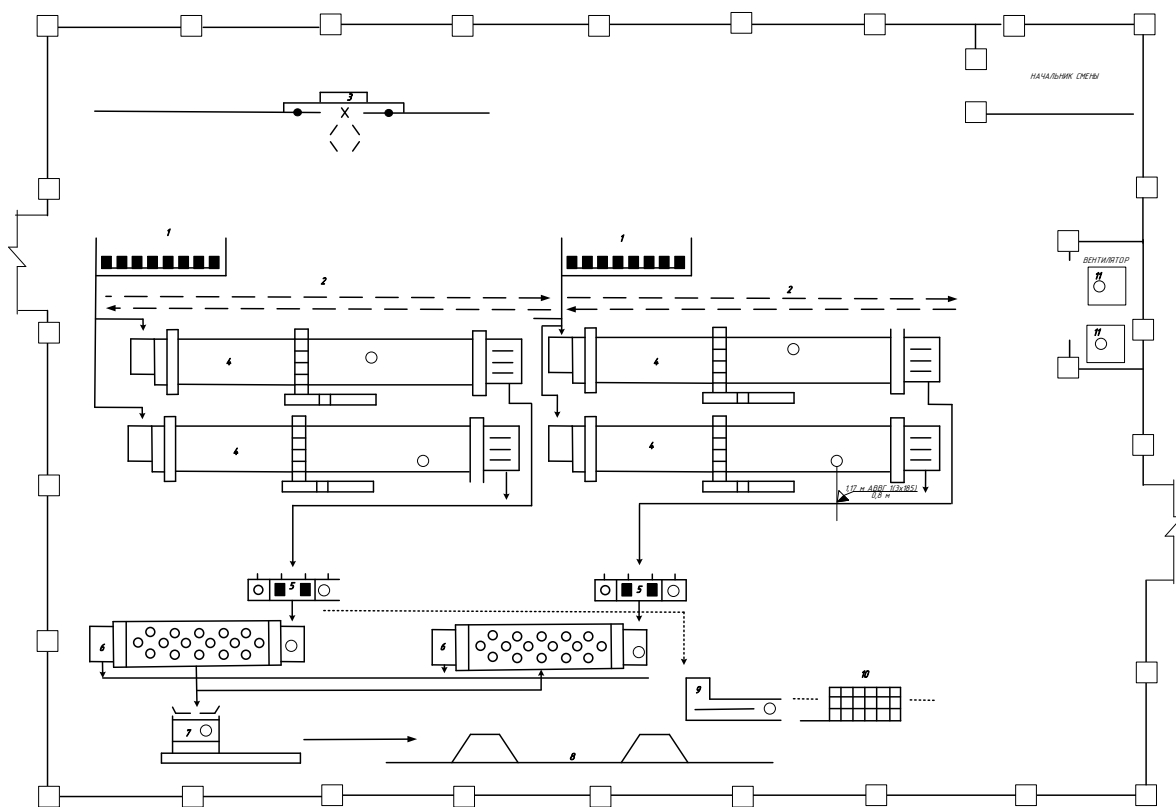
Ген - план отделения переработки пластика и стекла
